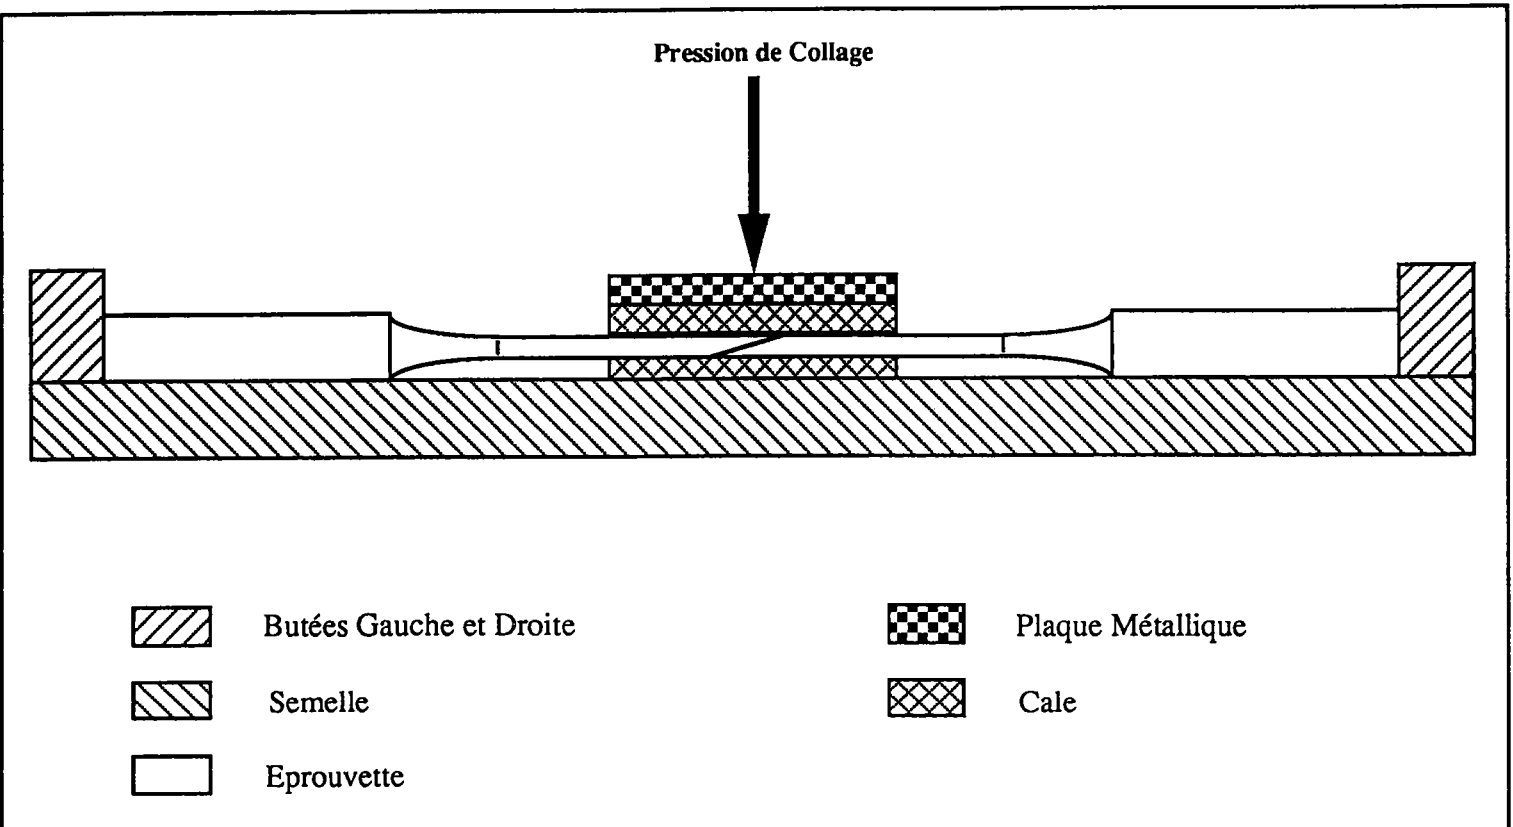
Montage de collage horizontal pour les angles d'aboutage de 45° , 60° et 75° .
